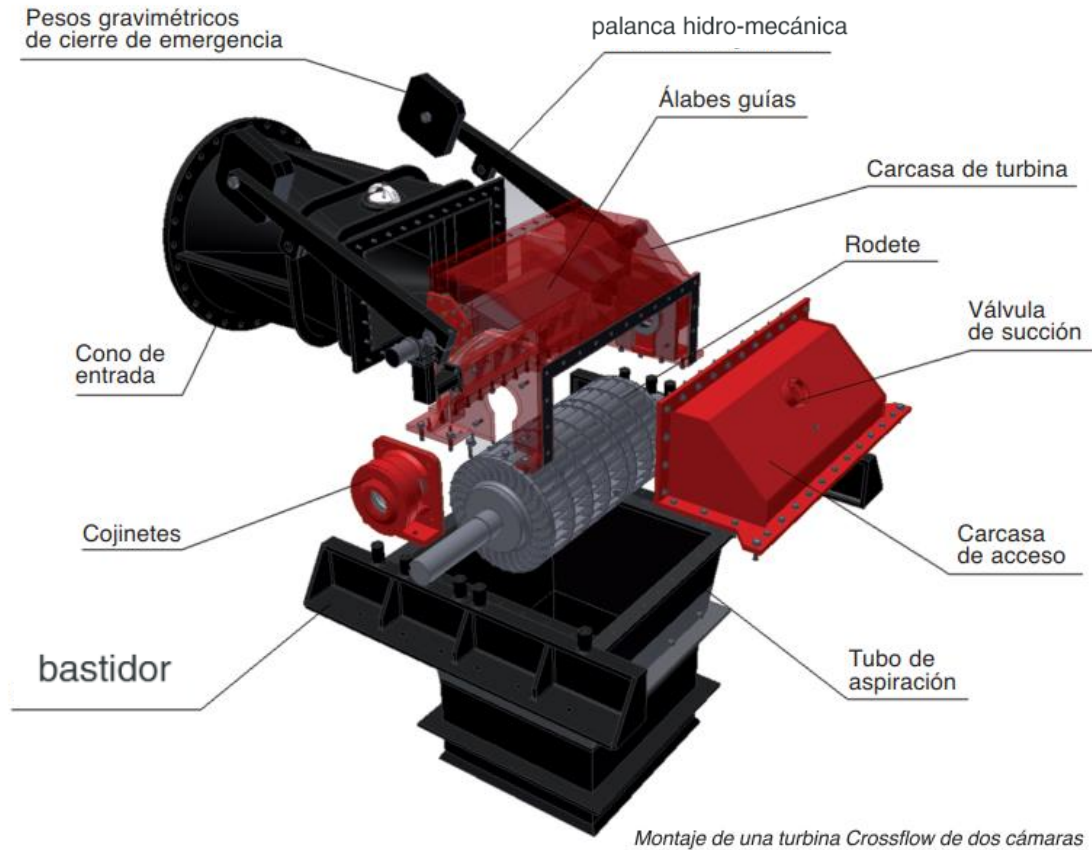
Diagrama de explosión Turbina Ossbeger. Fuente [2.14]
